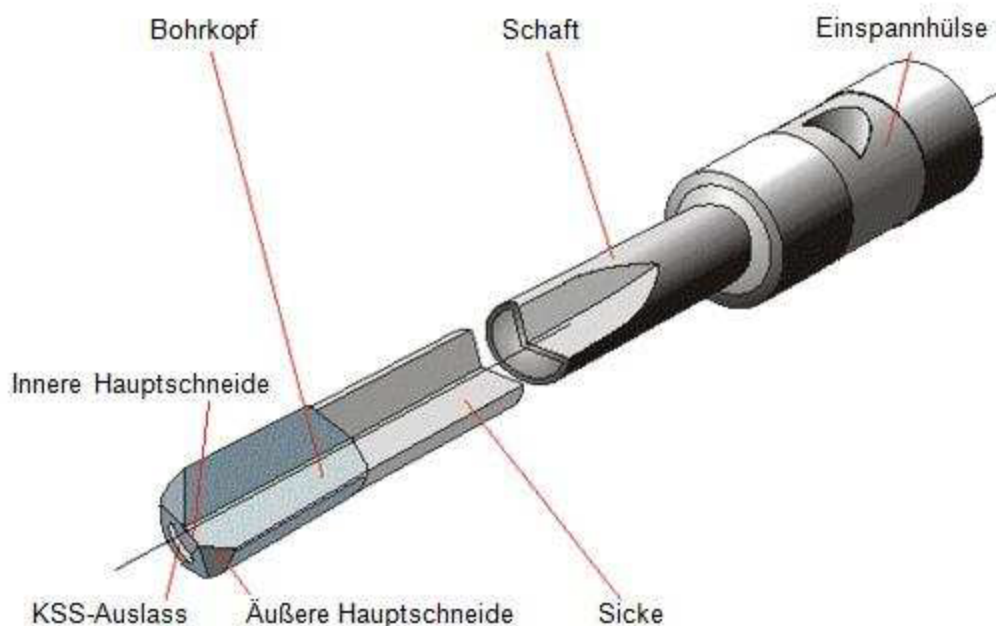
Einlippentiefbohrwerkzeug /27/
